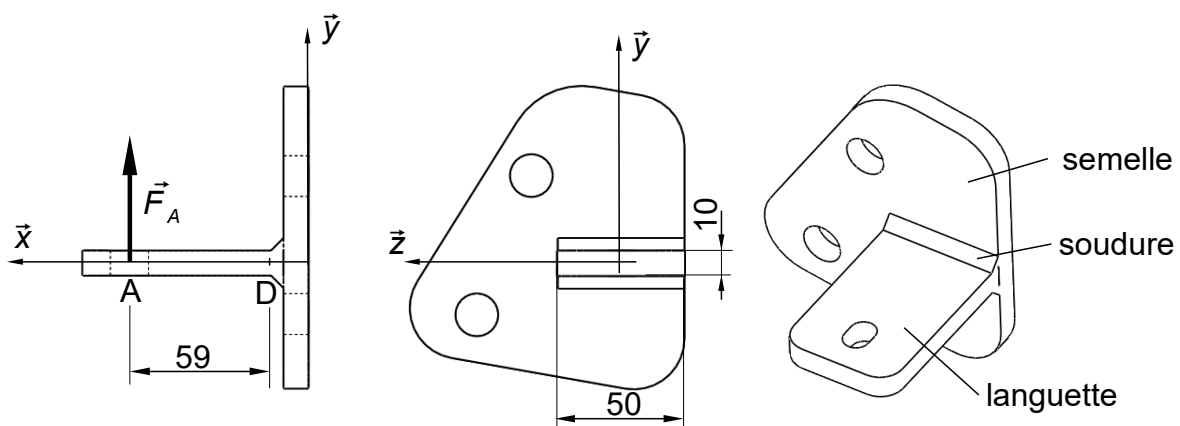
géométrie et chargement de l'équerre (dimensions en millimètres)
